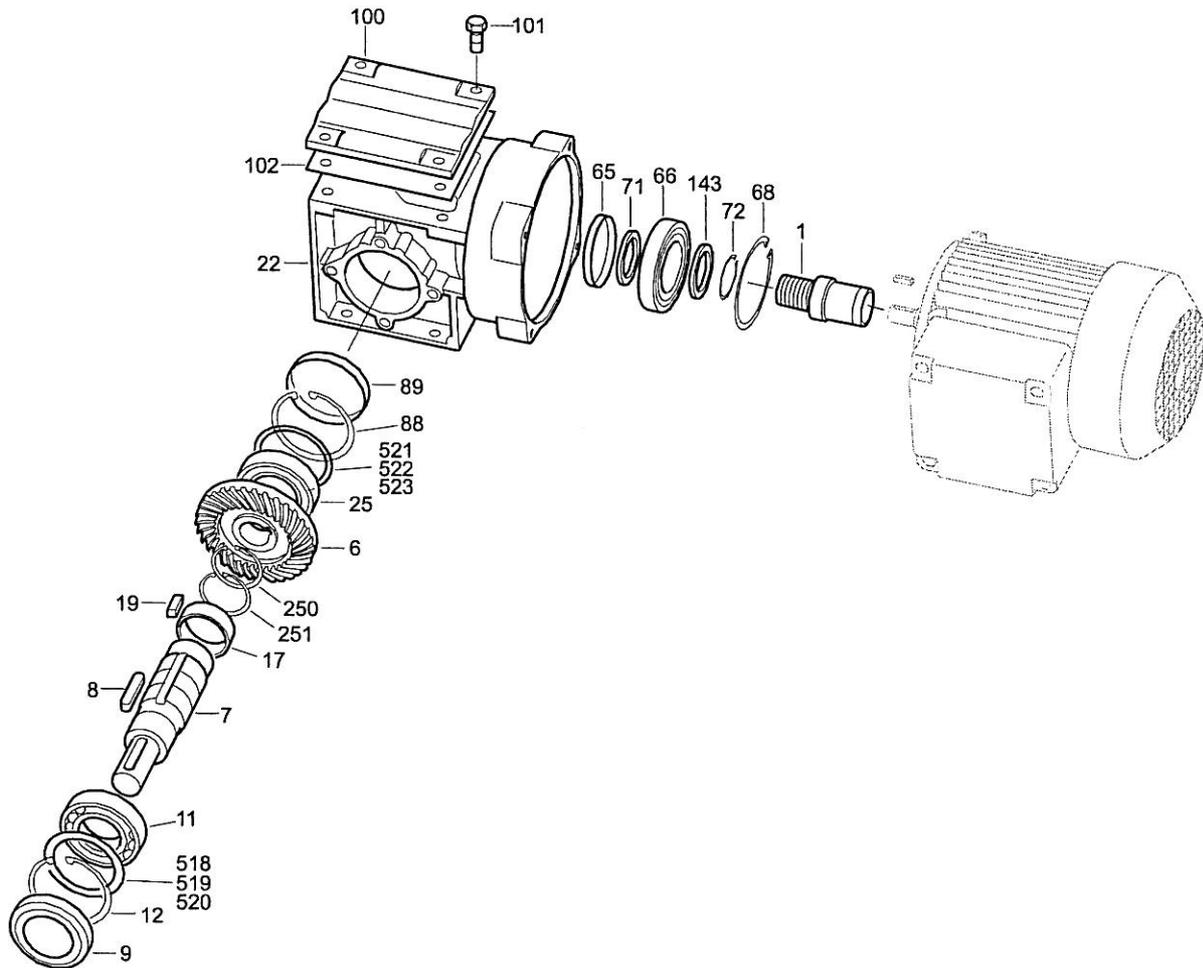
Prinzipieller Aufbau SPIROPLAN®-Getriebe
